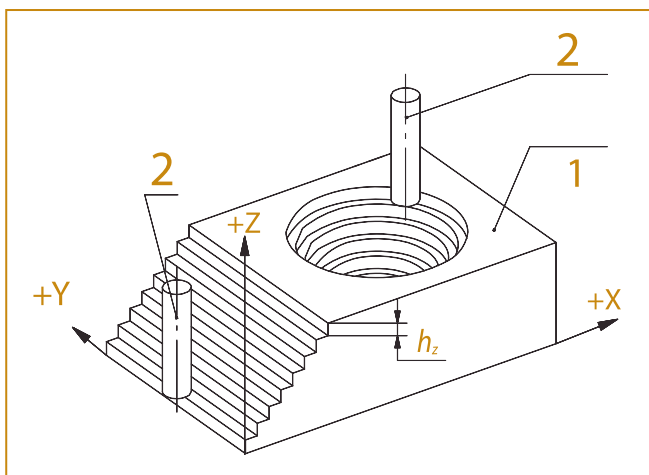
Схемы 2,5-координатного фрезерования объемных изделий на станке с ЧПУ, где 1 – заготовка; 2 – фреза
